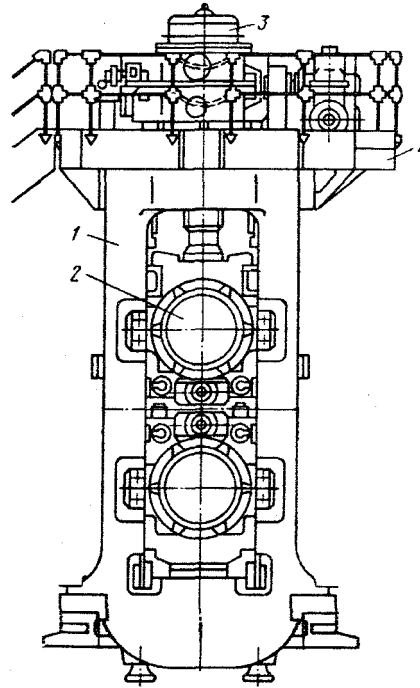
Загальний вид робочої кліті прокатного стану
